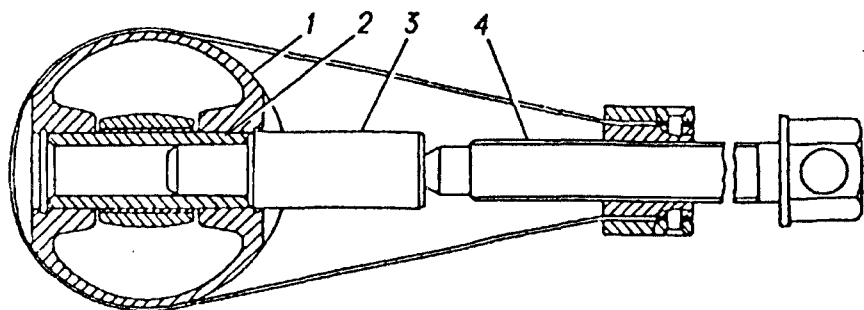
Выпрессовка поршневого пальца из поршня с помощью приспособления 6999-7678:
